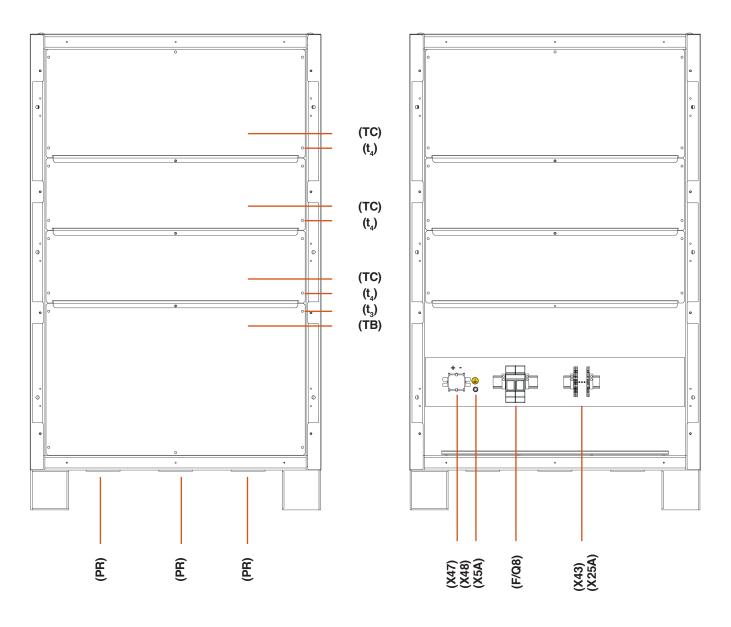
Vista frontal armario de baterías de 605x805x1315 mm.
